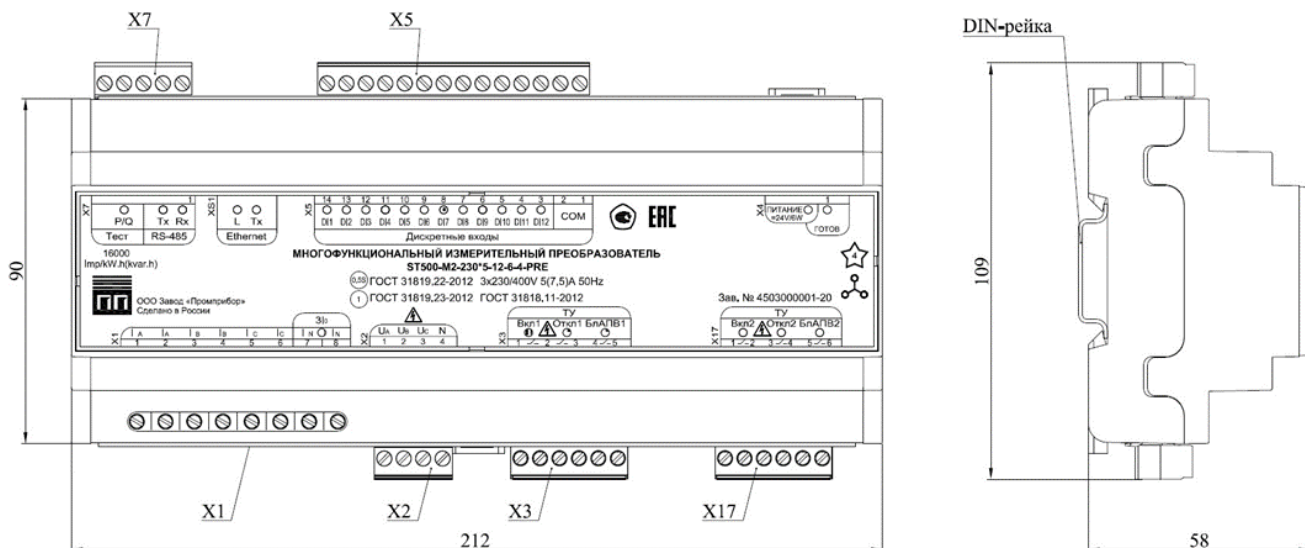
Внешний вид и габаритные размеры МИП
